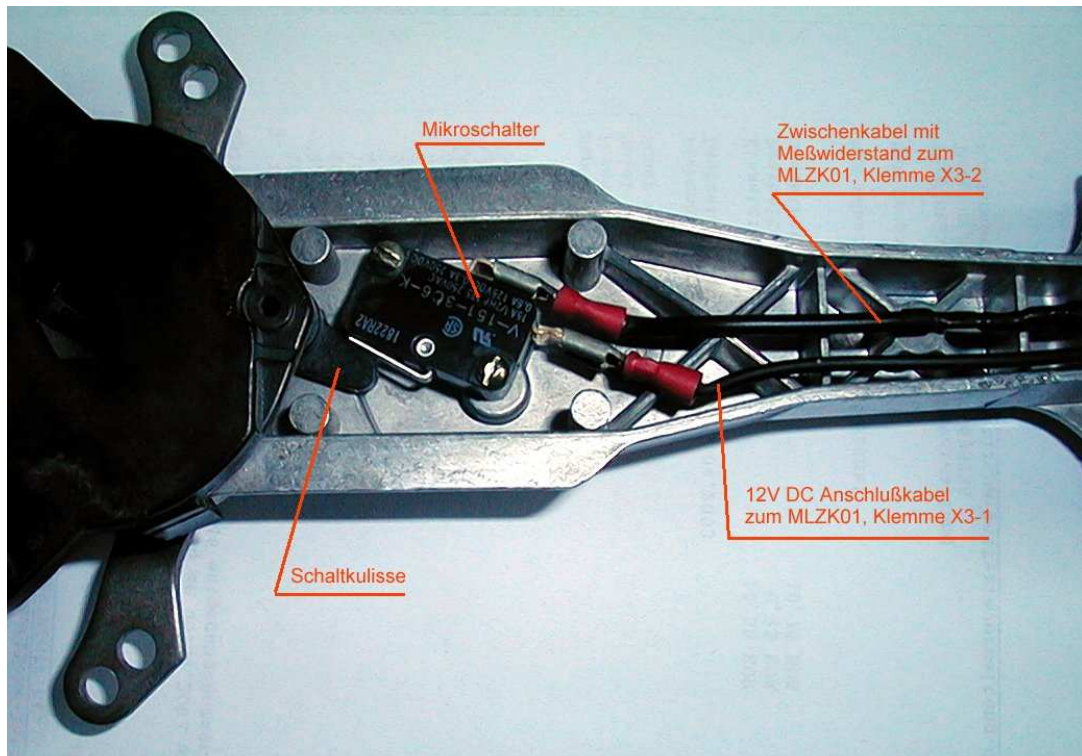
, geöffneter Motor-/Getriebschalthebel mit eingebautem Mikroschalter
